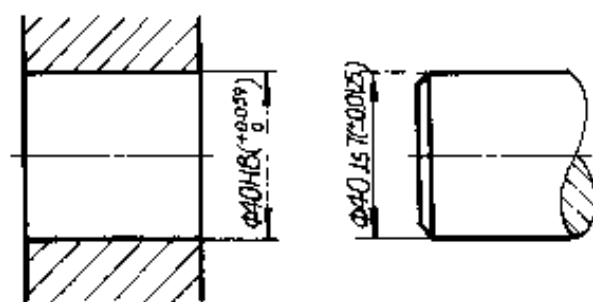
零件图上公差带代号与极限偏差的标注
